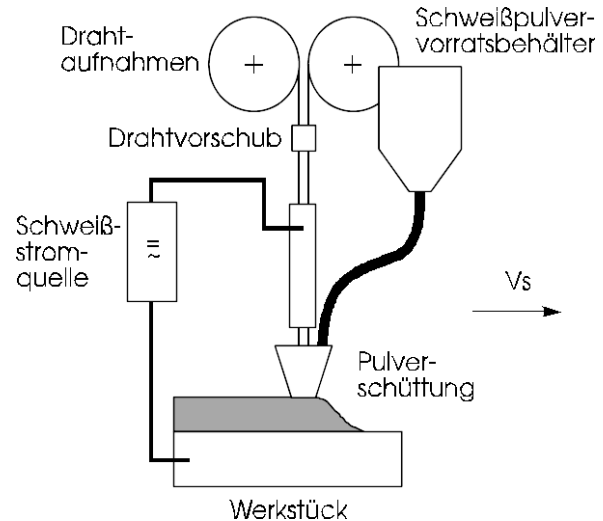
Prinzip des UP-Doppeldrahtschweißens.
